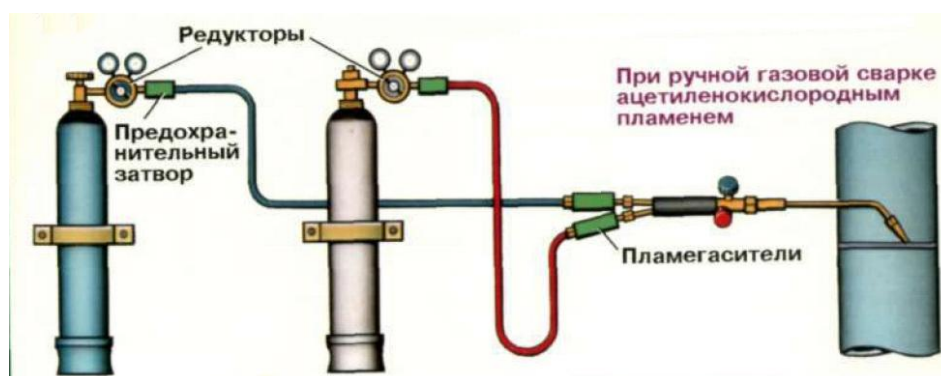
Газопламенная сварка (оборудование)
